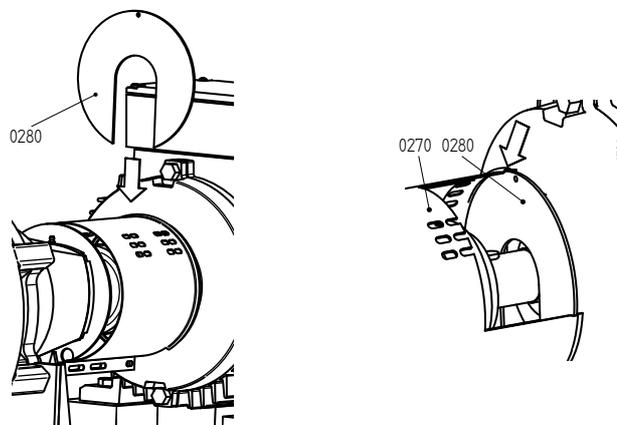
Montare lo scudo d'assemblaggio a lato del motore.
